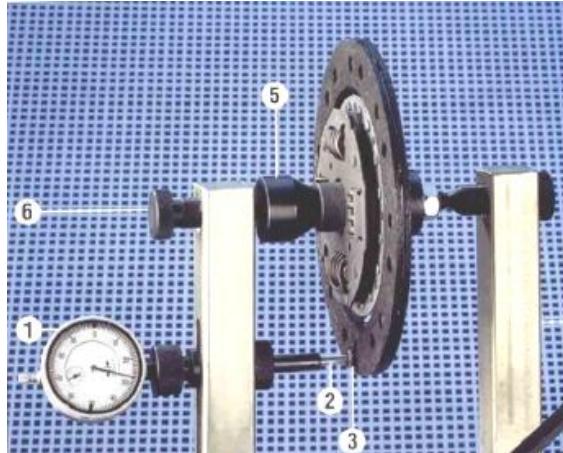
Проверка биения рабочей поверхности ведомого диска.
